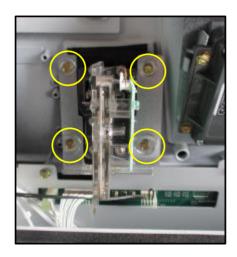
Emplacement Encore 500S des vis de plaque du lecteur de carte
